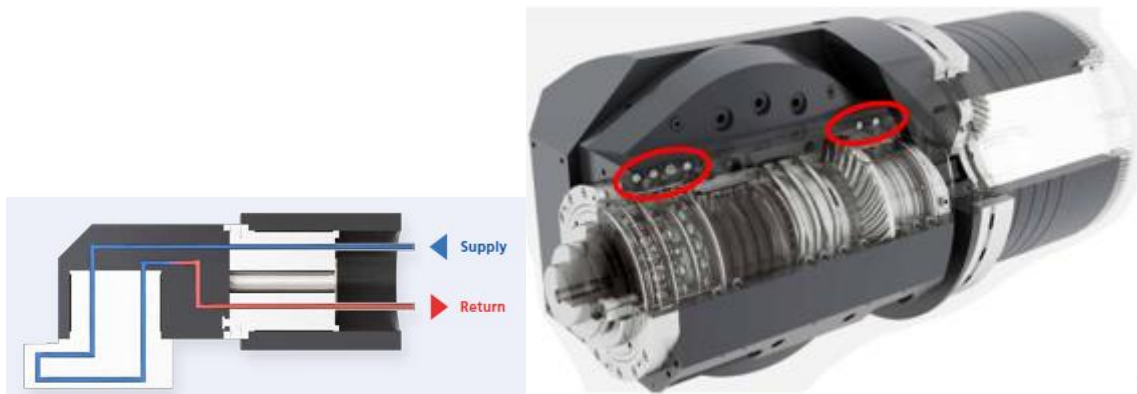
Reálné mazací zařízení od firmy Woerner [13]
